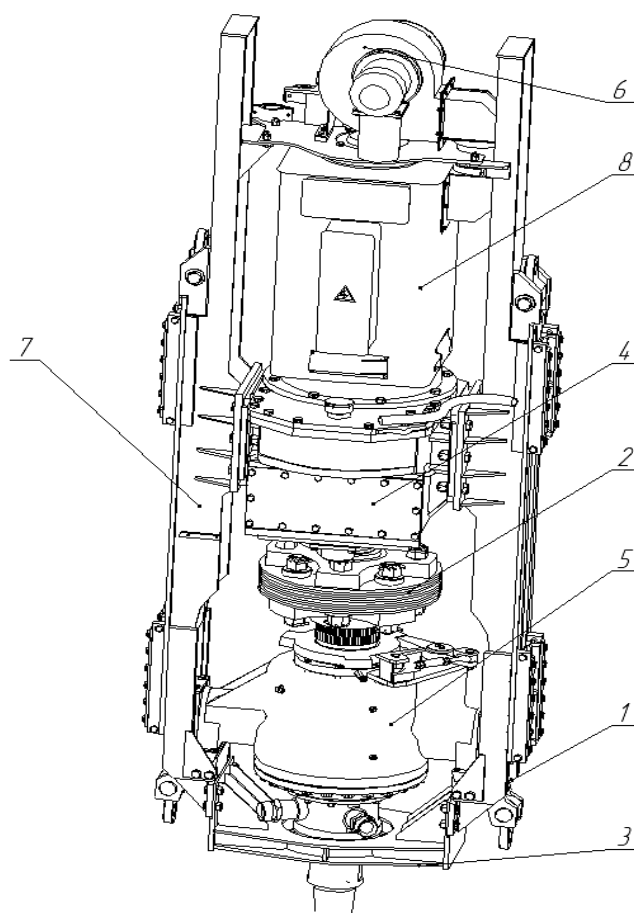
Головка бурового снаряда: 1 – ползун; 2 – муфта шинно-зубчатая; 3 – траверса; 4 – редуктор вращателя; 5 – узел опорный; 6 – установка вентиляционная; 7 – каретка; 8 – электродвигатель
